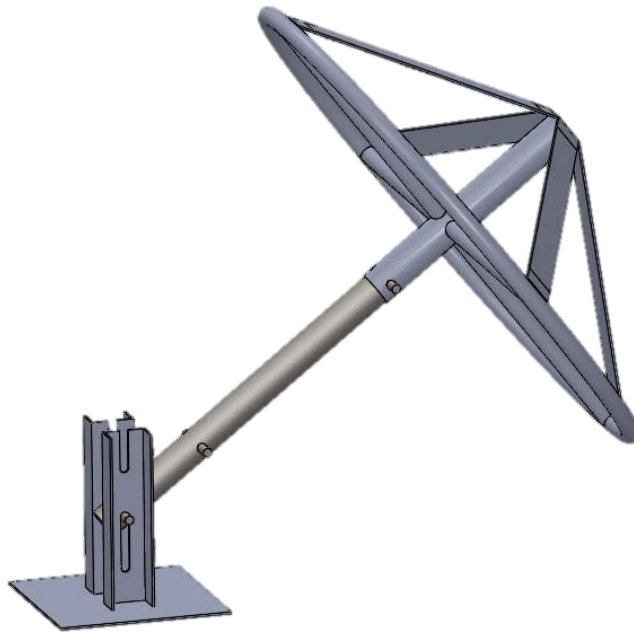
Movimiento de desmontaje de soporte de cornetas.
